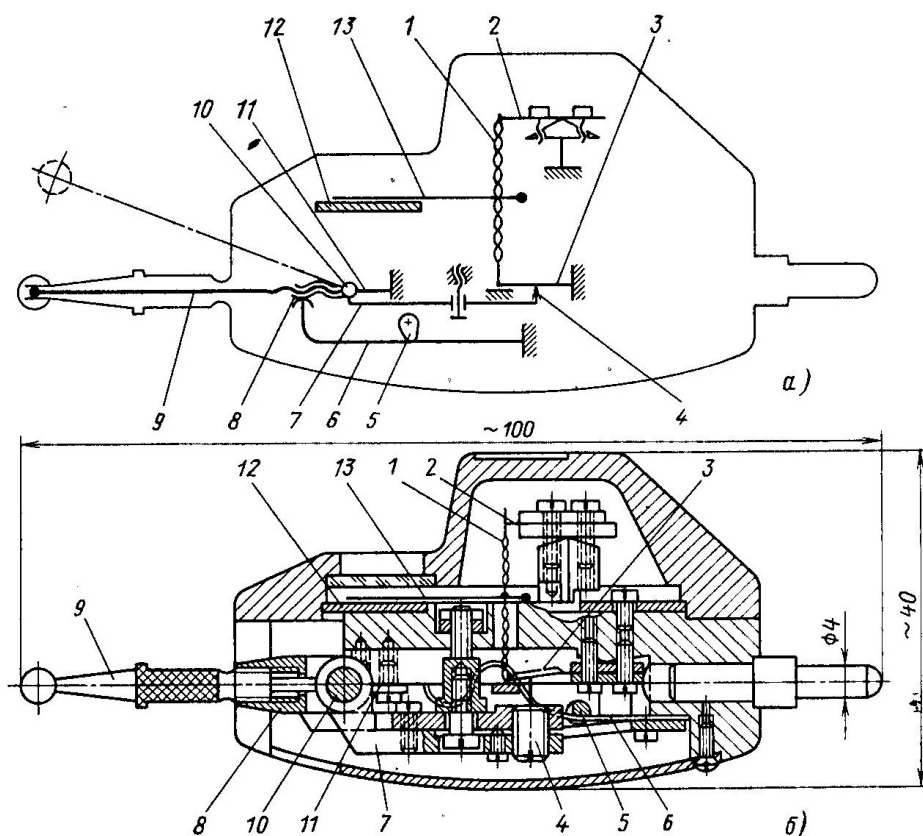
Рычажно-пружинная измерительная головка-миникатор: а – схема; б – конструкция
